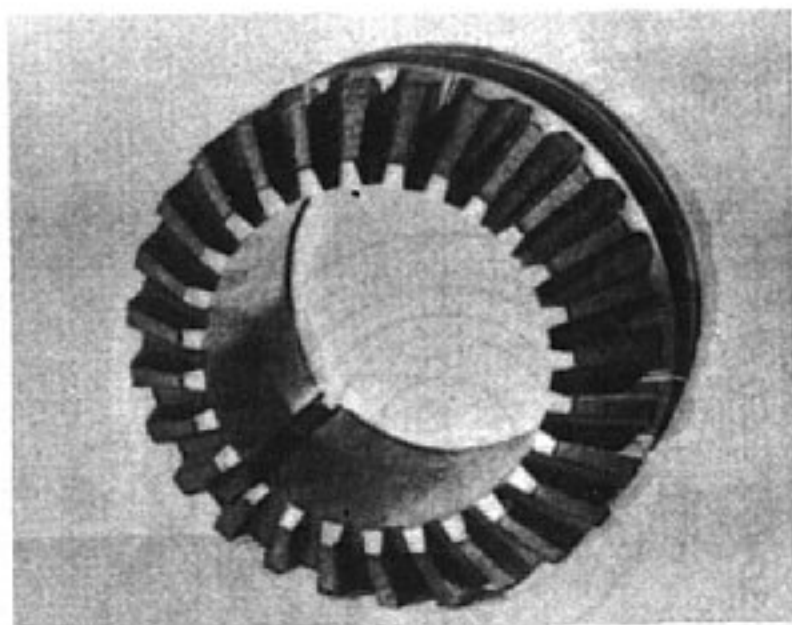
Rueda dentada cónica. (The Fellows Gear Shaper Company.)
